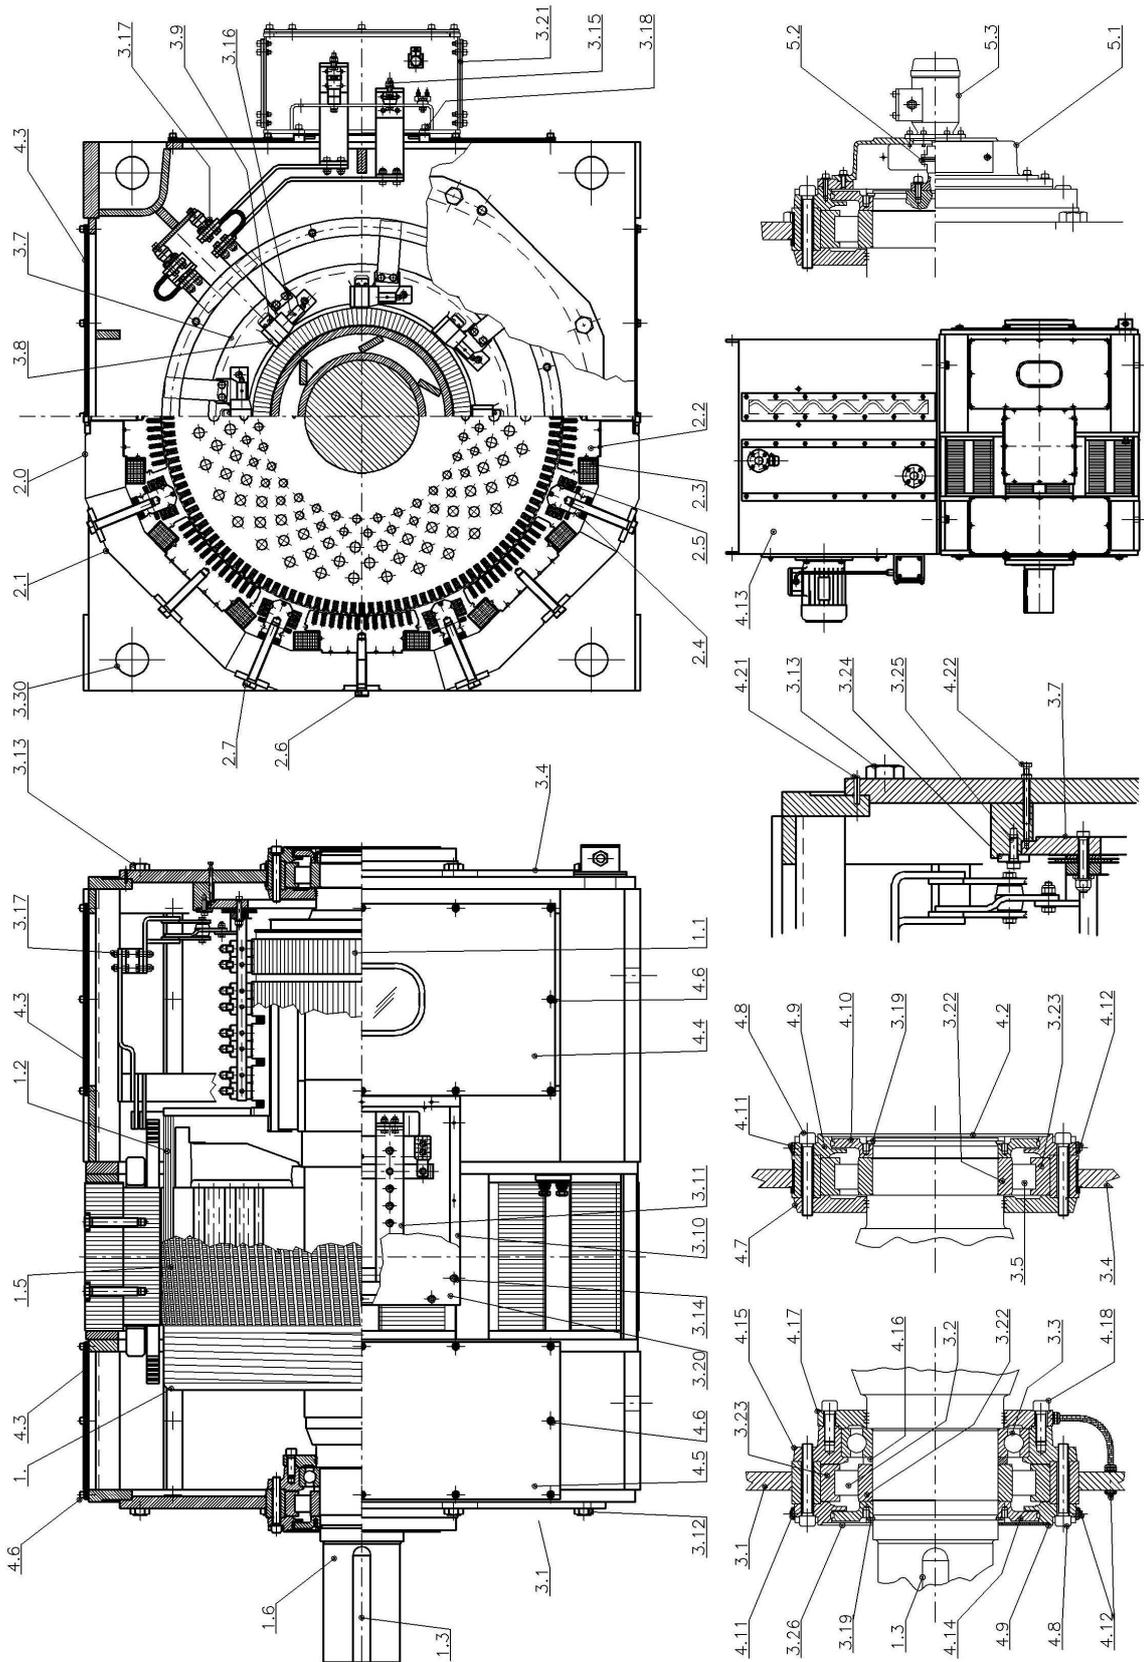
Croquis indicatif d'ensemble pour moteurs NP 710-800 (Pour la nomenclature voir fig. 10.5)
